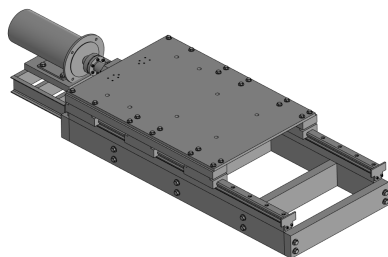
Общий вид привода поперечных подач станка (модели станка)
